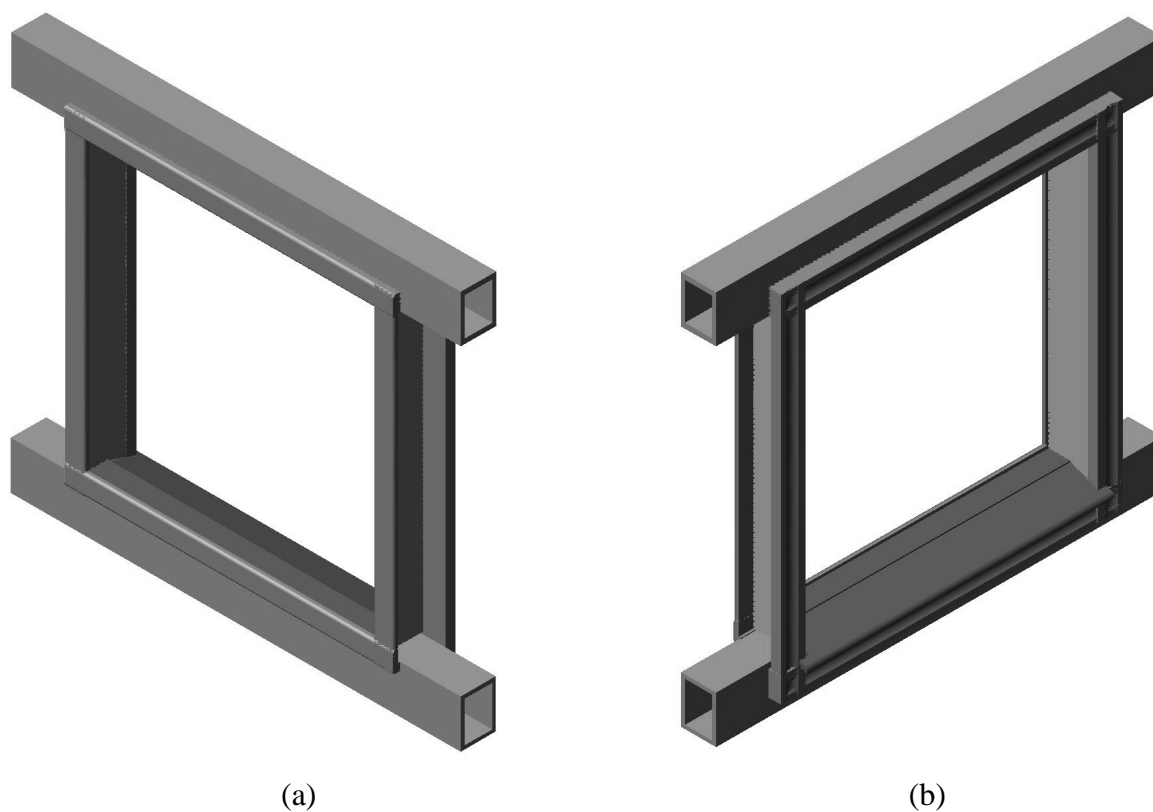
Projeto 03, vista 3d da face interna (a) e vista 3d da face externa (b).
